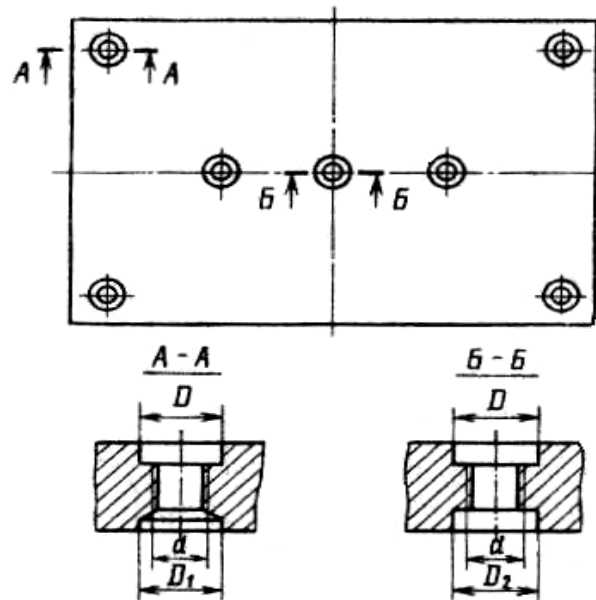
Форма и расположение крепежных отверстий в базовых плитах
